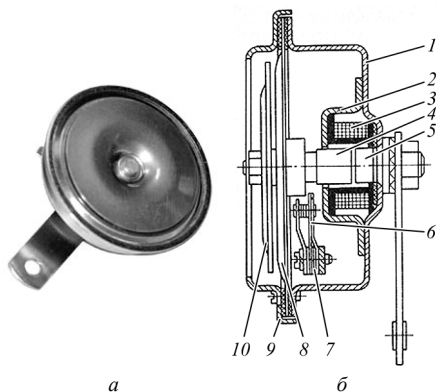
Безрупорный звуковой сигнал: *а* – внешний вид; *б* – устройство; 1 – корпус; 2 – ярмо; 3 – катушка; 4 – якорь; 5 – сердечник; 6 – держатель; 7 – прерыватель; 8 – мембрана; 9 – указатель поворота; 10 – резонатор
